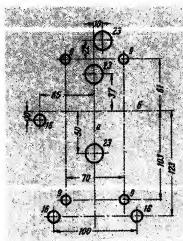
Сверление отверстий для установки на изоляционных панелях контакторов типа КП 523 и КП 533 с задним присоединением
